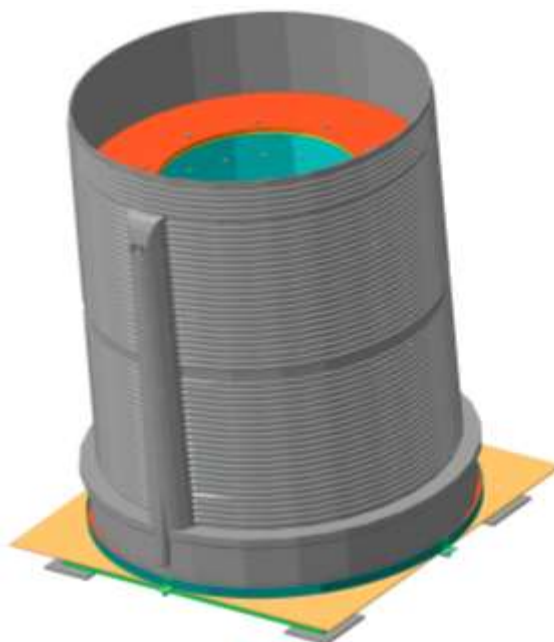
ВВР, установленный на стенд для нагрева внутренней обечайки
